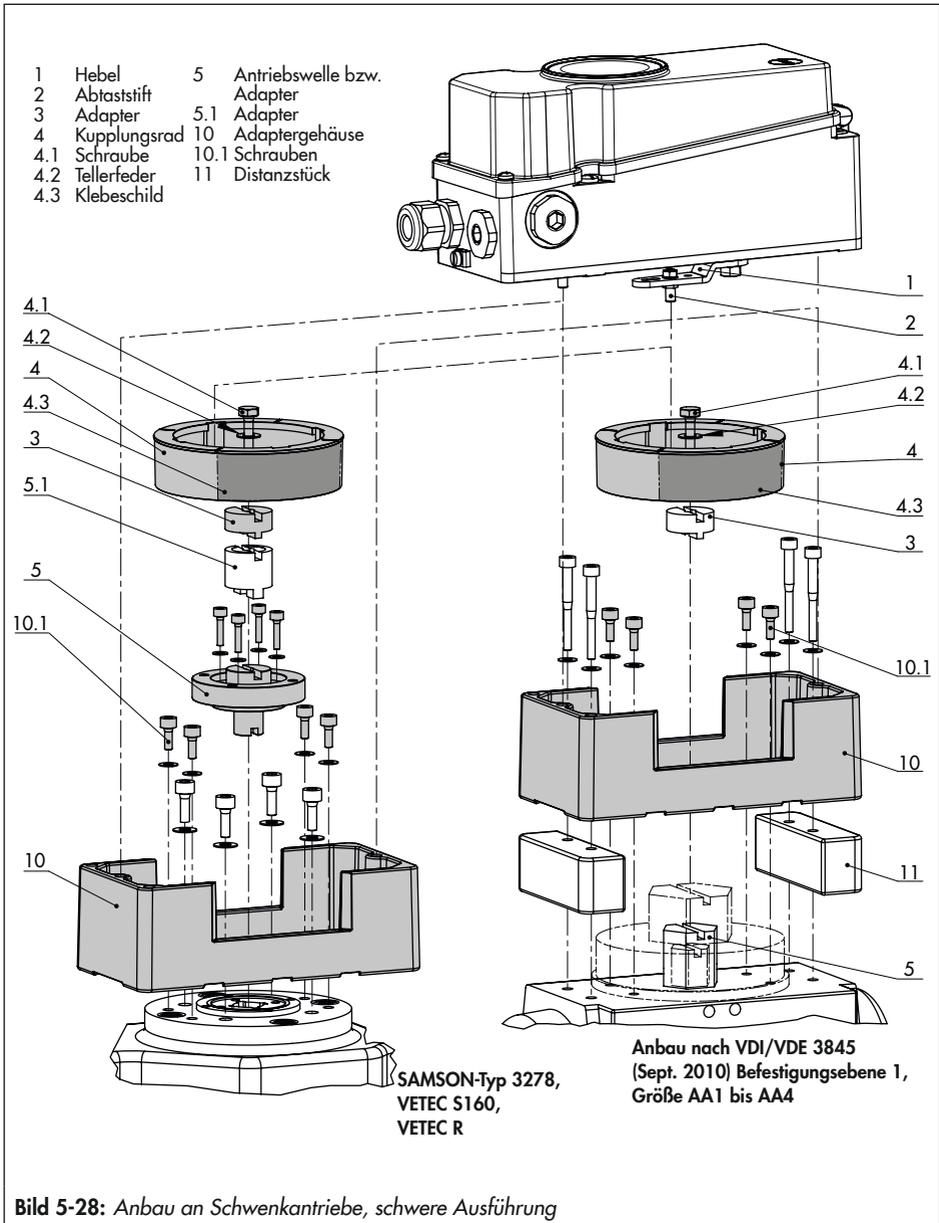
Anbau an Schwenkantriebe, schwere Ausführung
